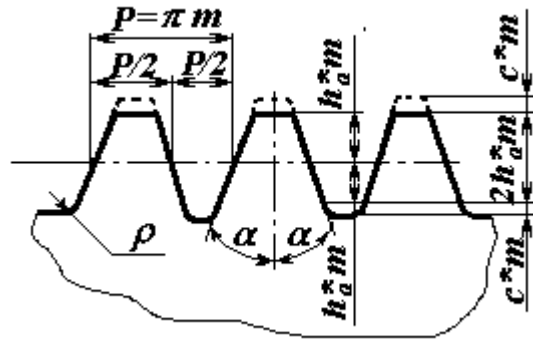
Параметри вихідного контуру зубонарізної рейки
